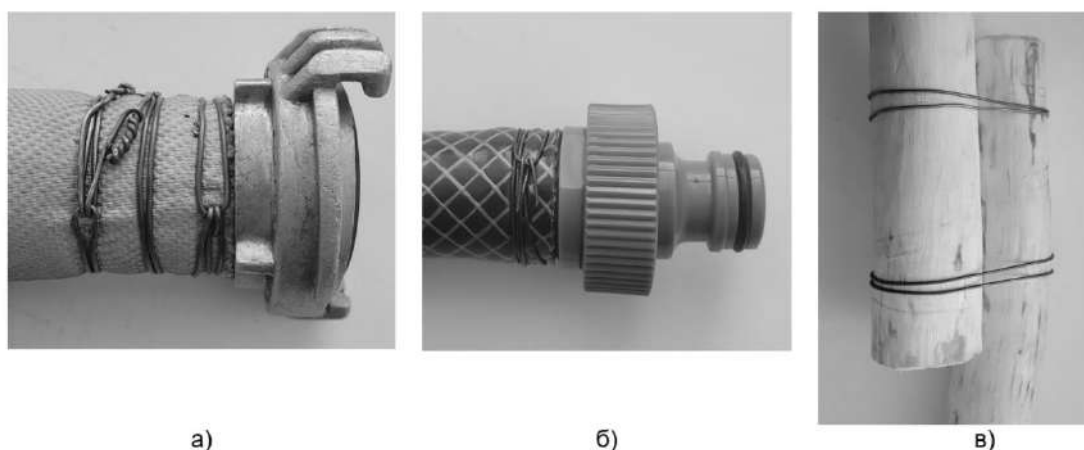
Специальное устройство для создания проволочного хомута на соединительной арматуре:
